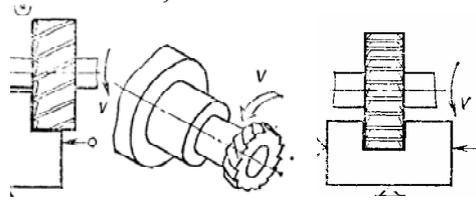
Отрезка заготовки на фрезерном станке дисковыми фрезами
